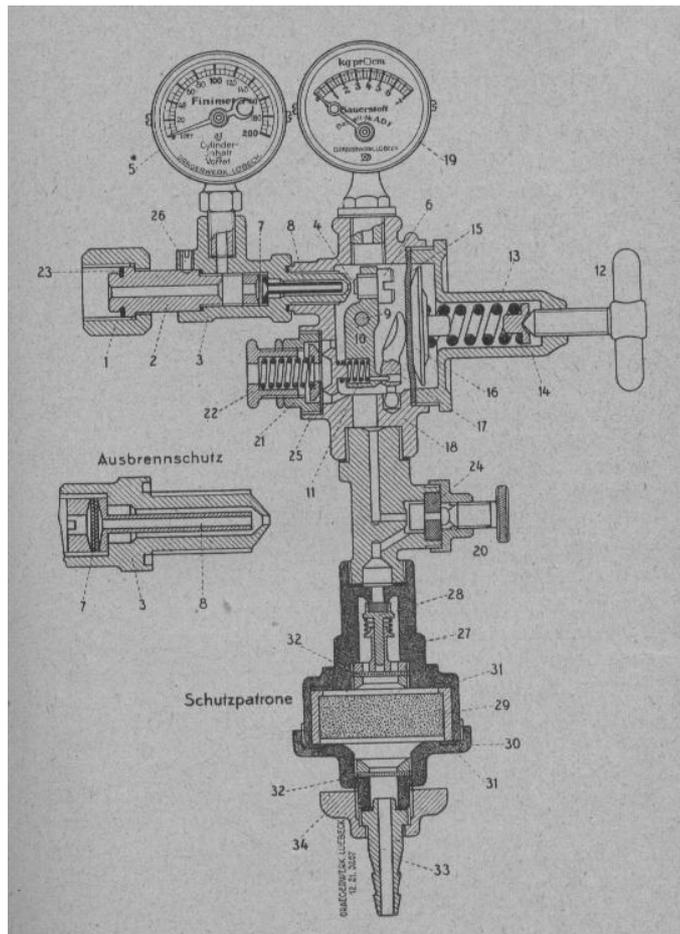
Druckgasreduzierventil für Schweißzwecke [113].
